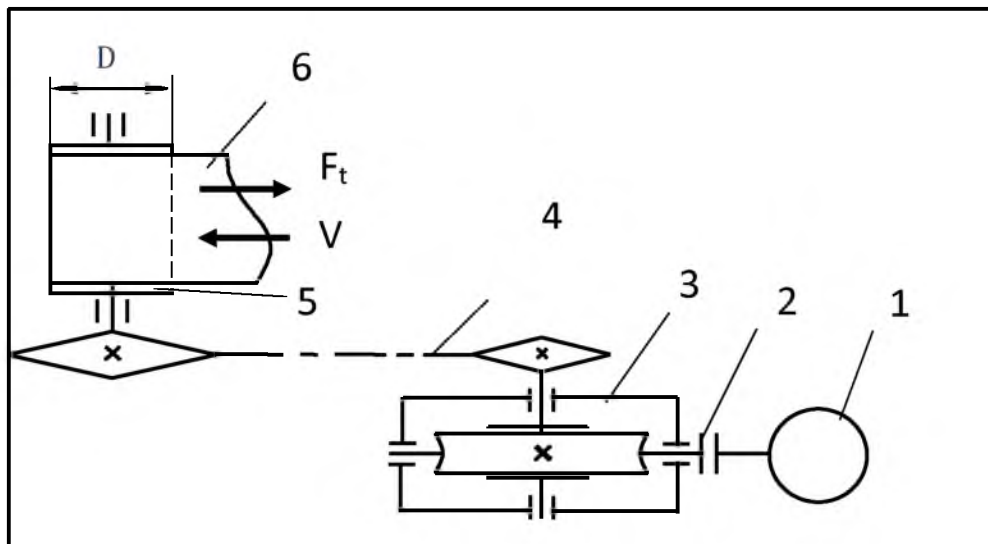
Кинематическая схема привода: 1 – электродвигатель; 2 – муфта; 3 – червячный редуктор; 4 – передача цепная; 5 – барабан; 6 – лента конвейера
